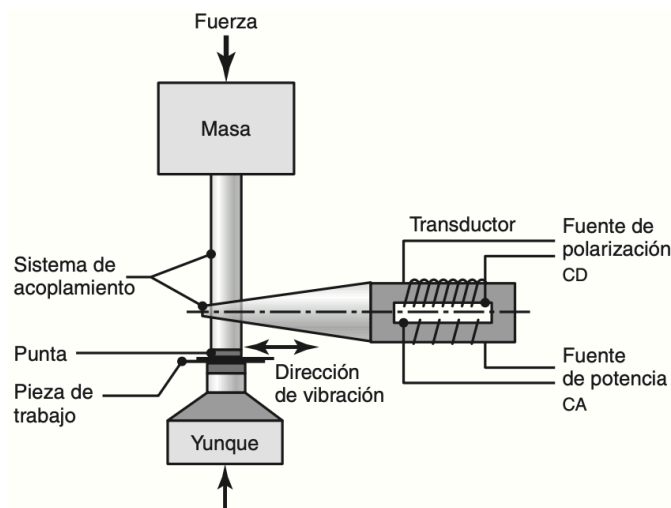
Proceso de soldadura ultrasónica. [26]
